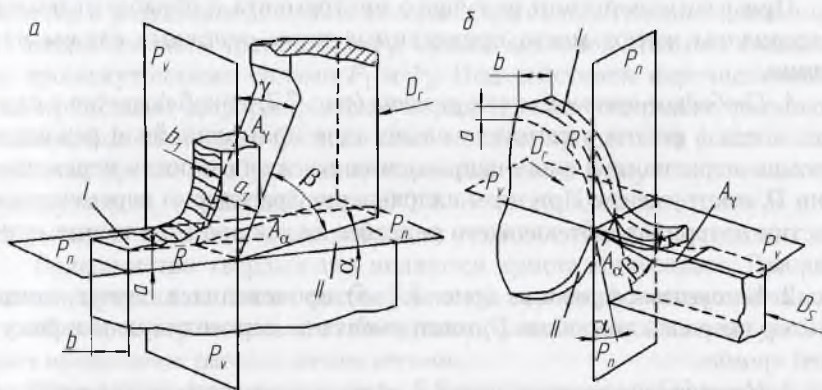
Геометрические параметры процесса резания при обработке плоской (а) и цилиндрической (б) поверхностей заготовок
